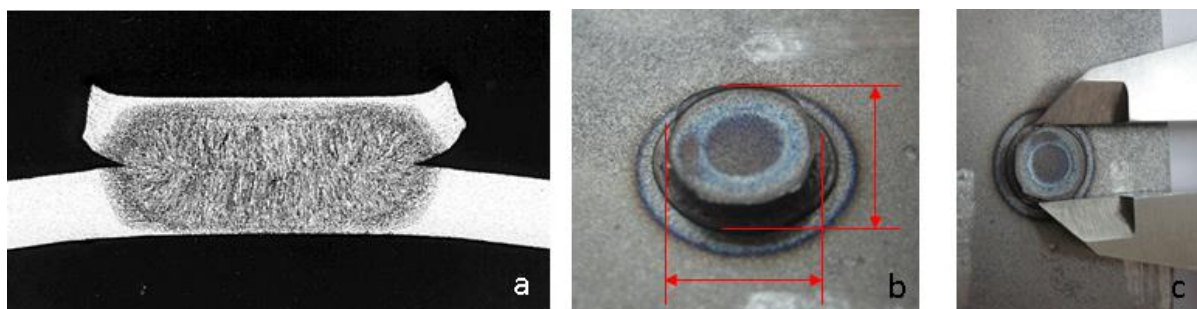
a. Sección transversal que muestra el exceso de material de la chapa, b: dimensiones de la soldadura a medir, c: posición correcta de la pinza Vernier. Fuente: TWI
